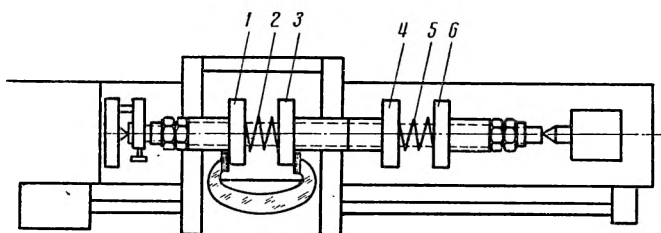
Схема специального станка для предварительной и окончательной доводки скоб
